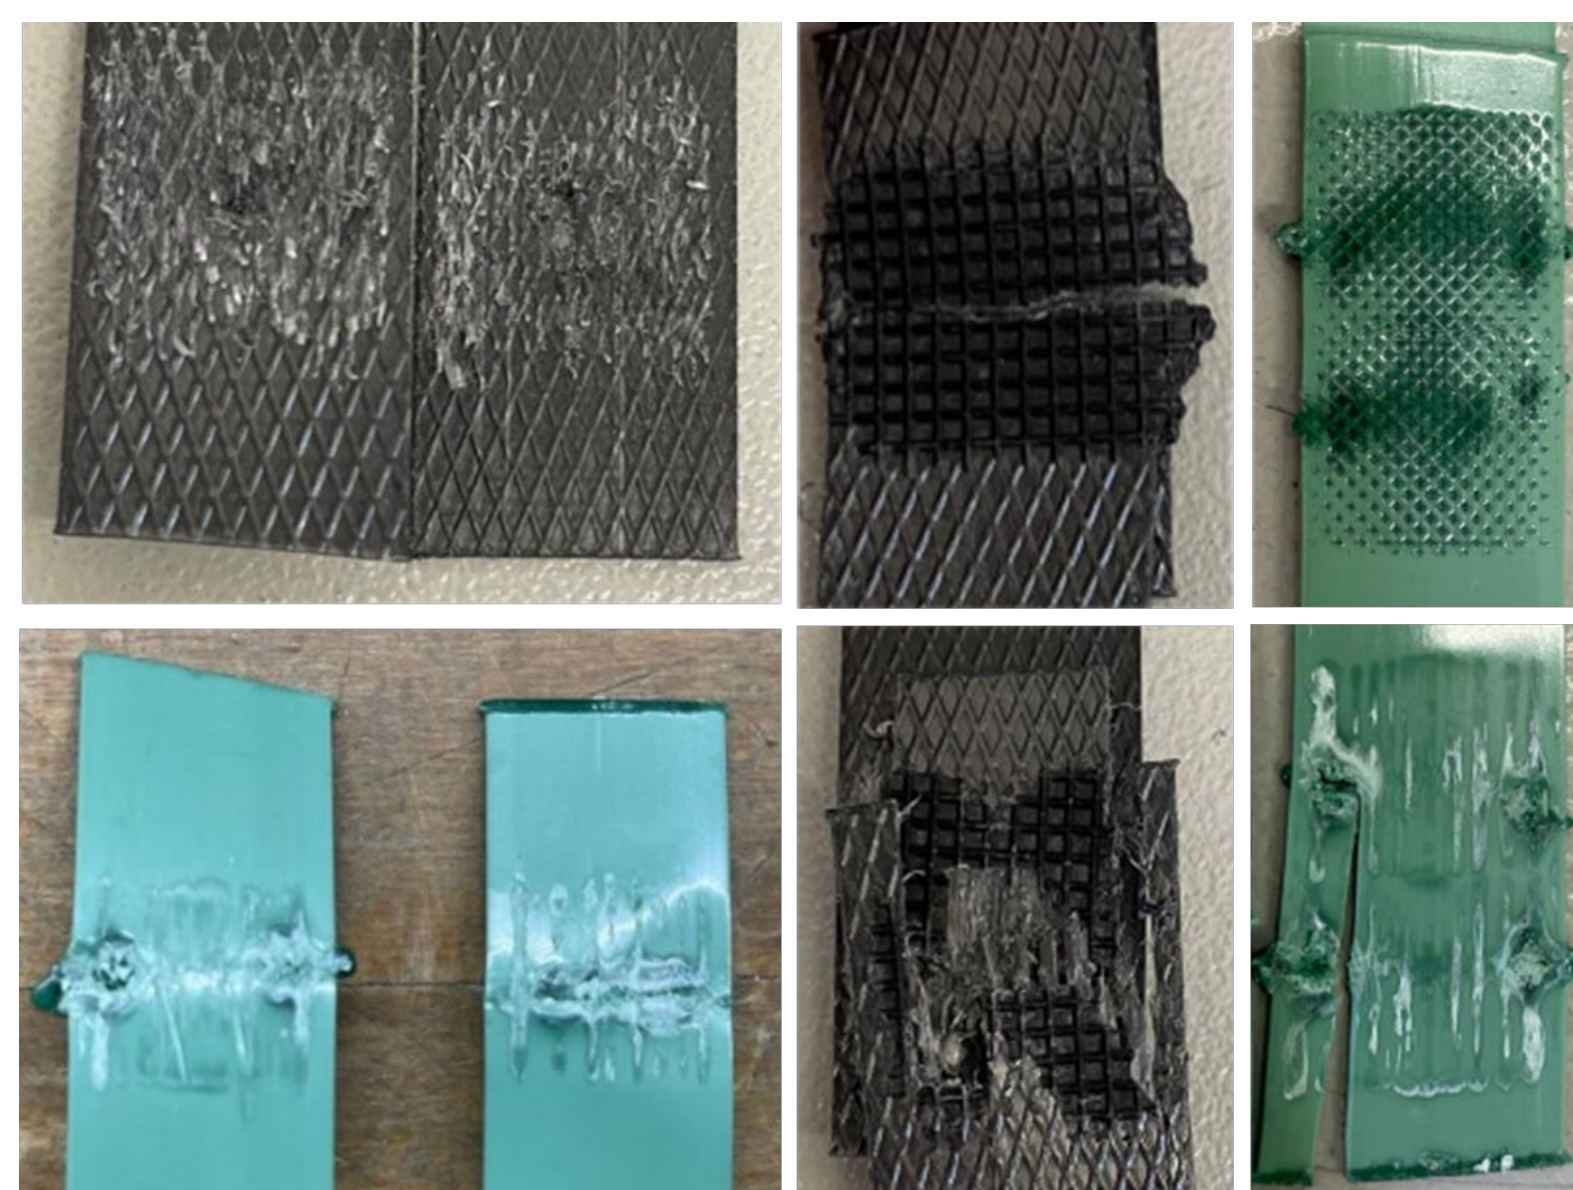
Bruchflächen verschiedener Schweißungen
